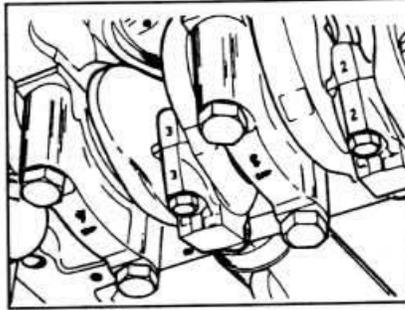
D.57. Метки идентификации крышки нижней головки шатуна и крышки коренного подшипника.
